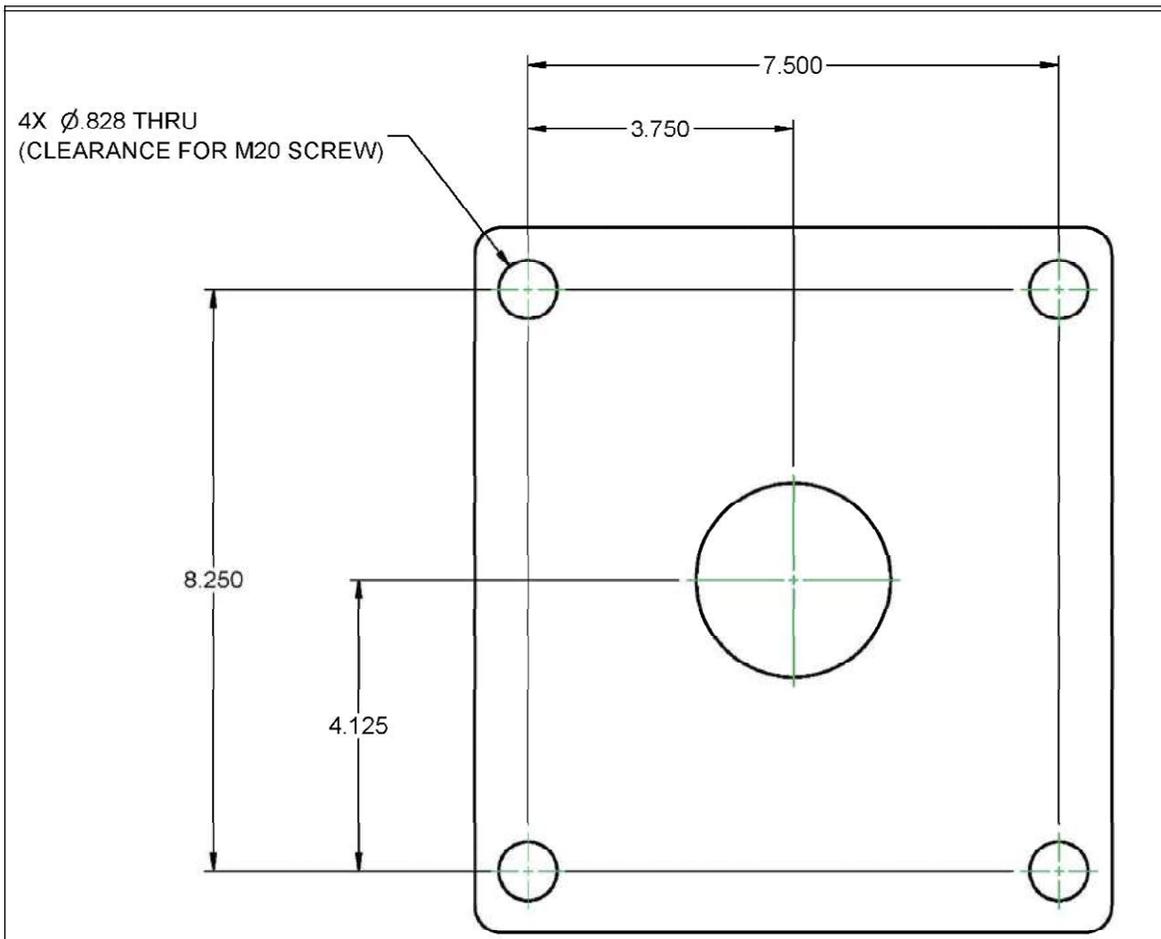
DIMENSIONS DES PLAQUES À SOUDER PAR POINTS
